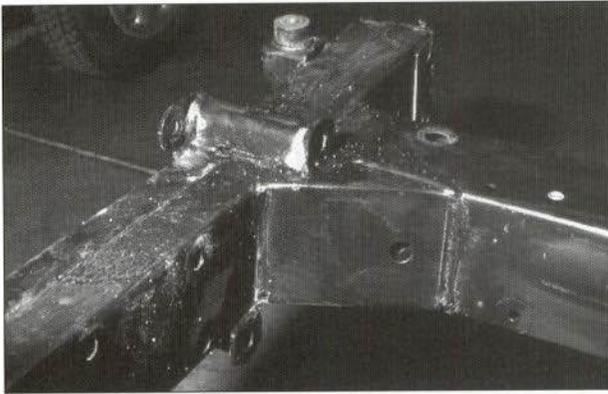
Detalle de unión soldada con escuadra de refuerzo.
